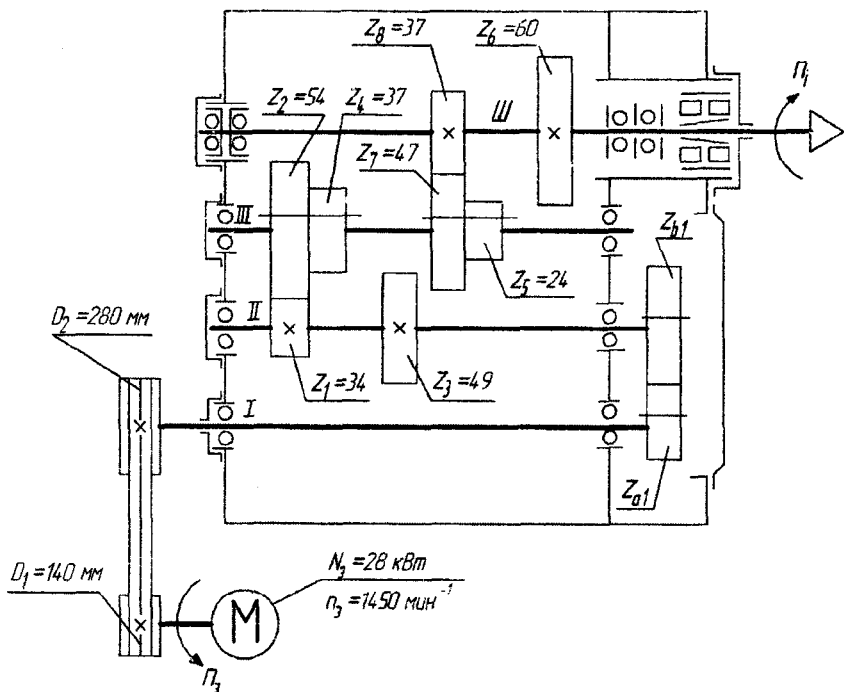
Кинематическая схема главного привода гидрокопировального полуавтомата модели 1722
